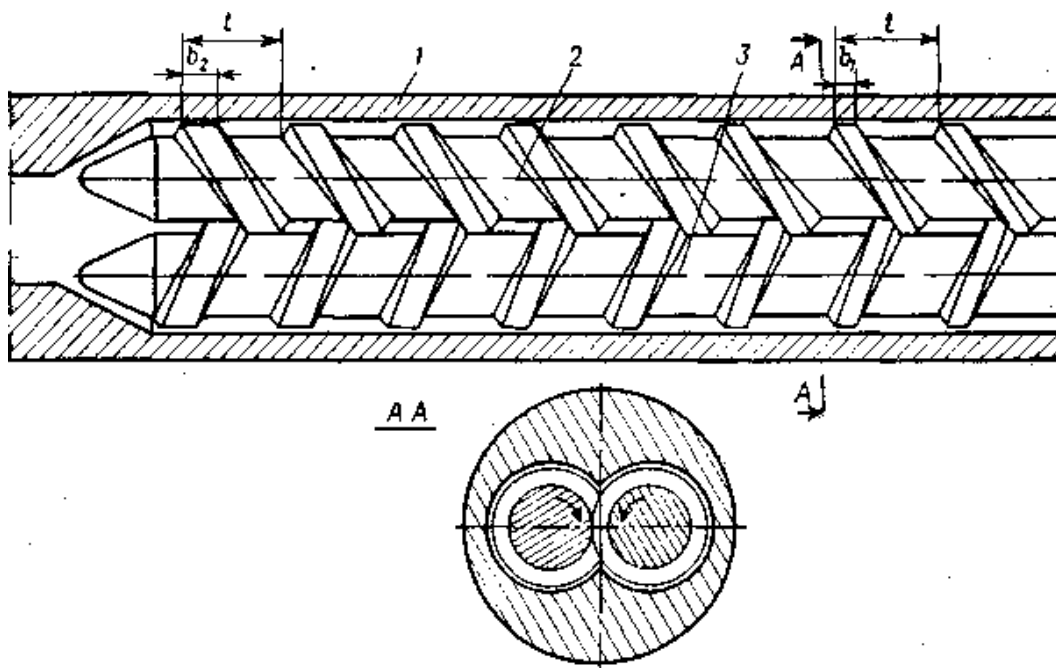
Черв'ячна пара двохчерв'ячного пресу:
